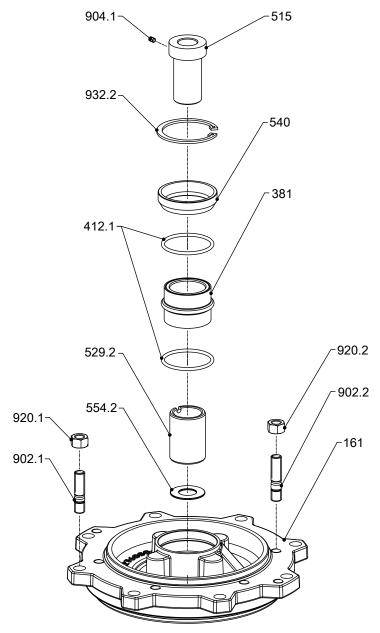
Монтаж крышки корпуса для подшипниковой опоры типоразмера VCS 40 и VCS 60
